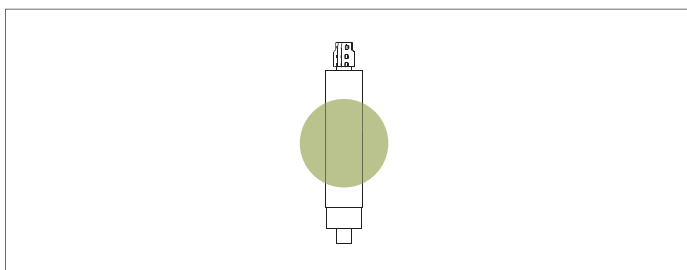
Установка защитных патрубков на вертикальный приводной вал
